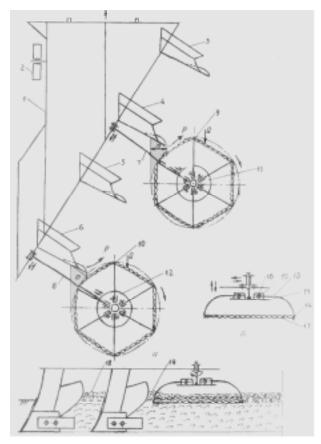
Комбинированный пахотный агрегат: I — рама; 2 — колесо; 3, 4, 5, 6 — корпуса; 7, 8 — кронштейны; 9, 10 — фрезы; 11, 12 — диски; 13 — стойка; 14 — лапа; 15 — держатель; 16 — стопорные болты; 17 — цепь; 18, 19 — гребни почвы
